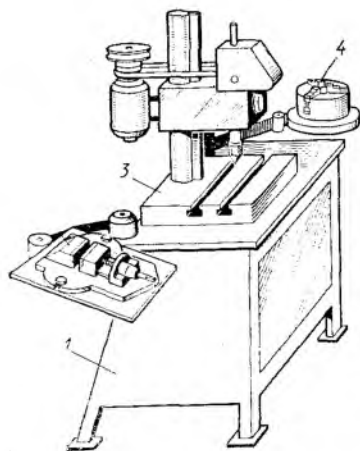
Приспособление для сверления деталей типа ось без разметки
